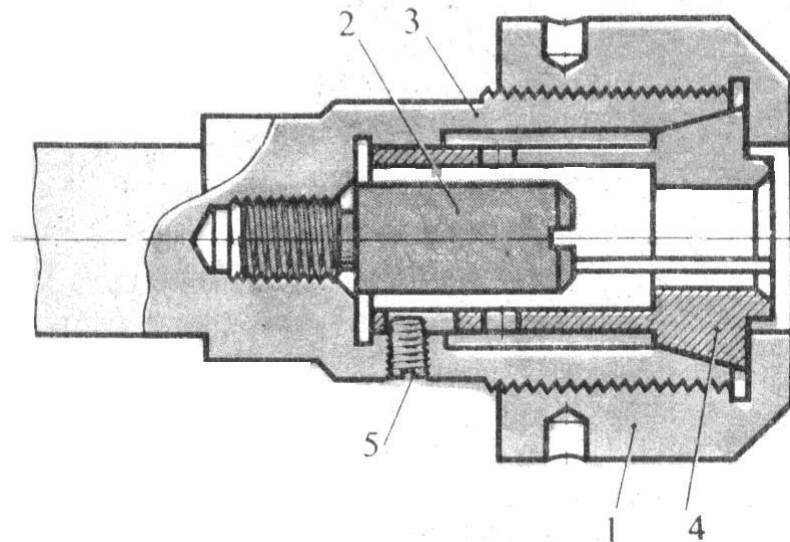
Цанговий патрон: 1 – натискна гайка, 2 – регульований упор, 3 – корпус, 4 – цанга, 5 – гвинт
